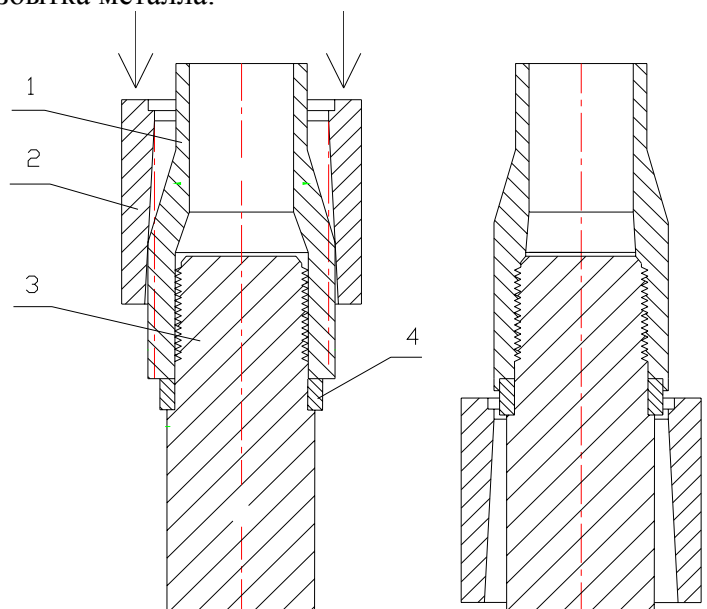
Схема штамповки резьбы на муфтовом конце переводника
